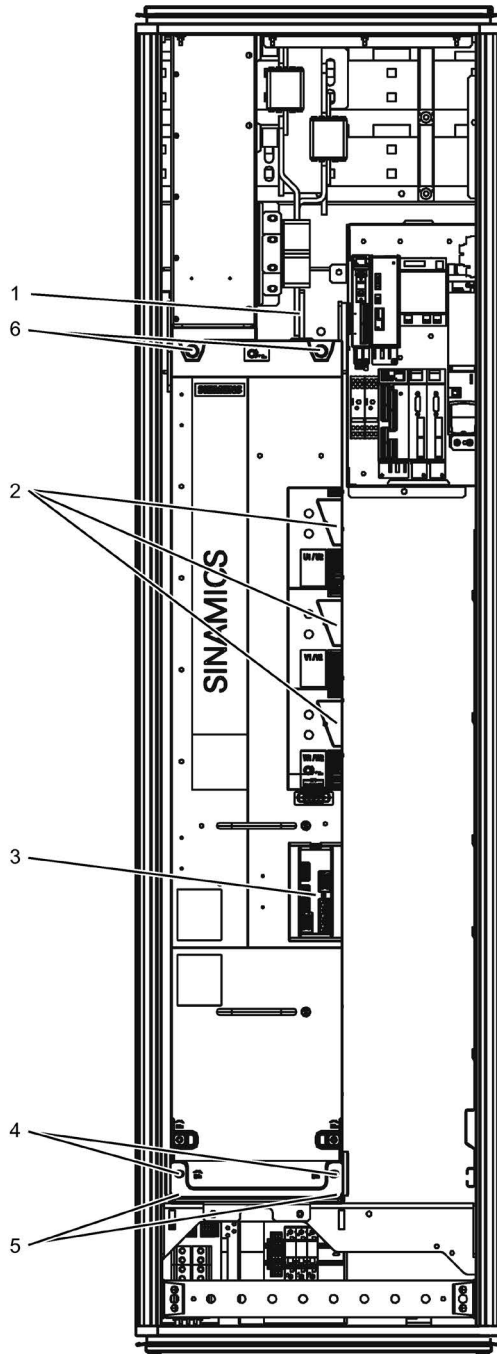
Замена модуля двигателя «шасси-2», типоразмер FS4
